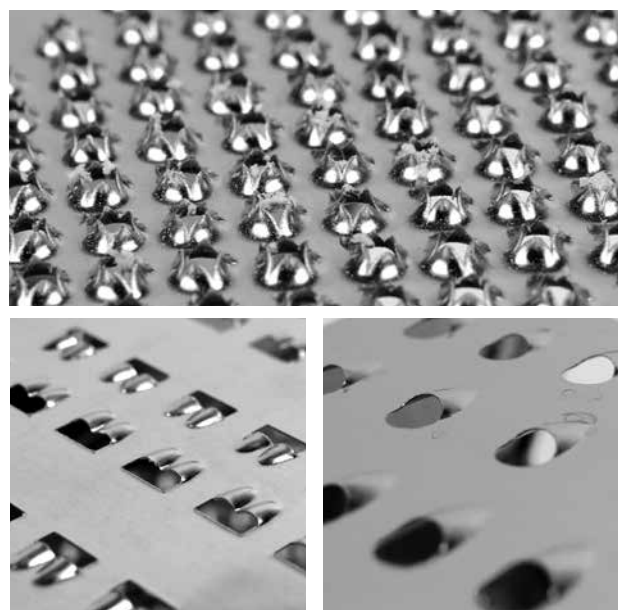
Schredder-Werkzeug. Oben Werkzeug A. Unten links Werkzeug B. Unten rechts Werkzeug C.
